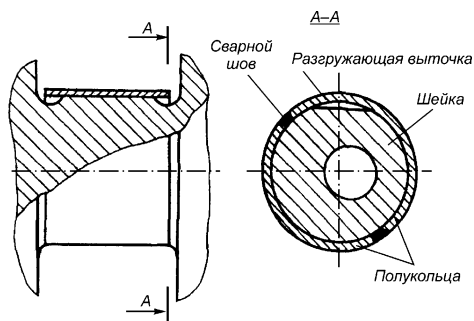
Шатунная шейка коленчатого вала двигателя, восстановленная приваркой стальных закаленных полуколец после конструктивно-технологической подготовки поверхности
